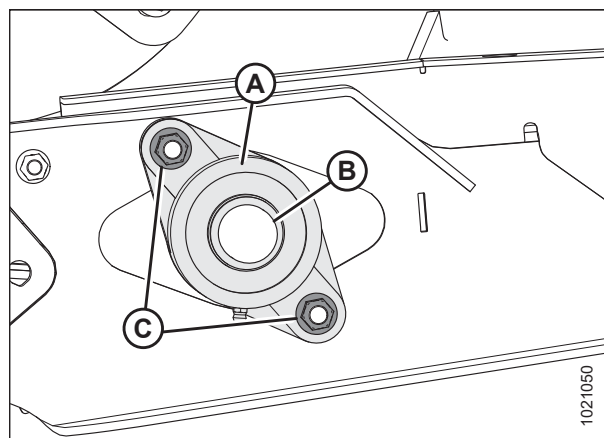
Подшипник приводного ролика подающего полотна
